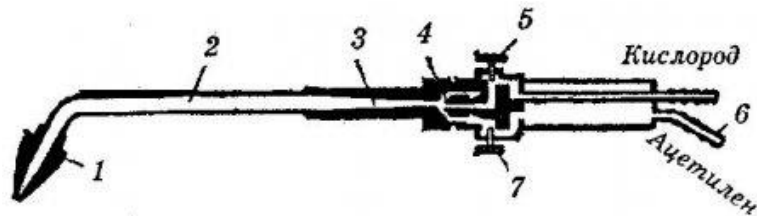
Конструкция инжекторной сварочной горелки:
